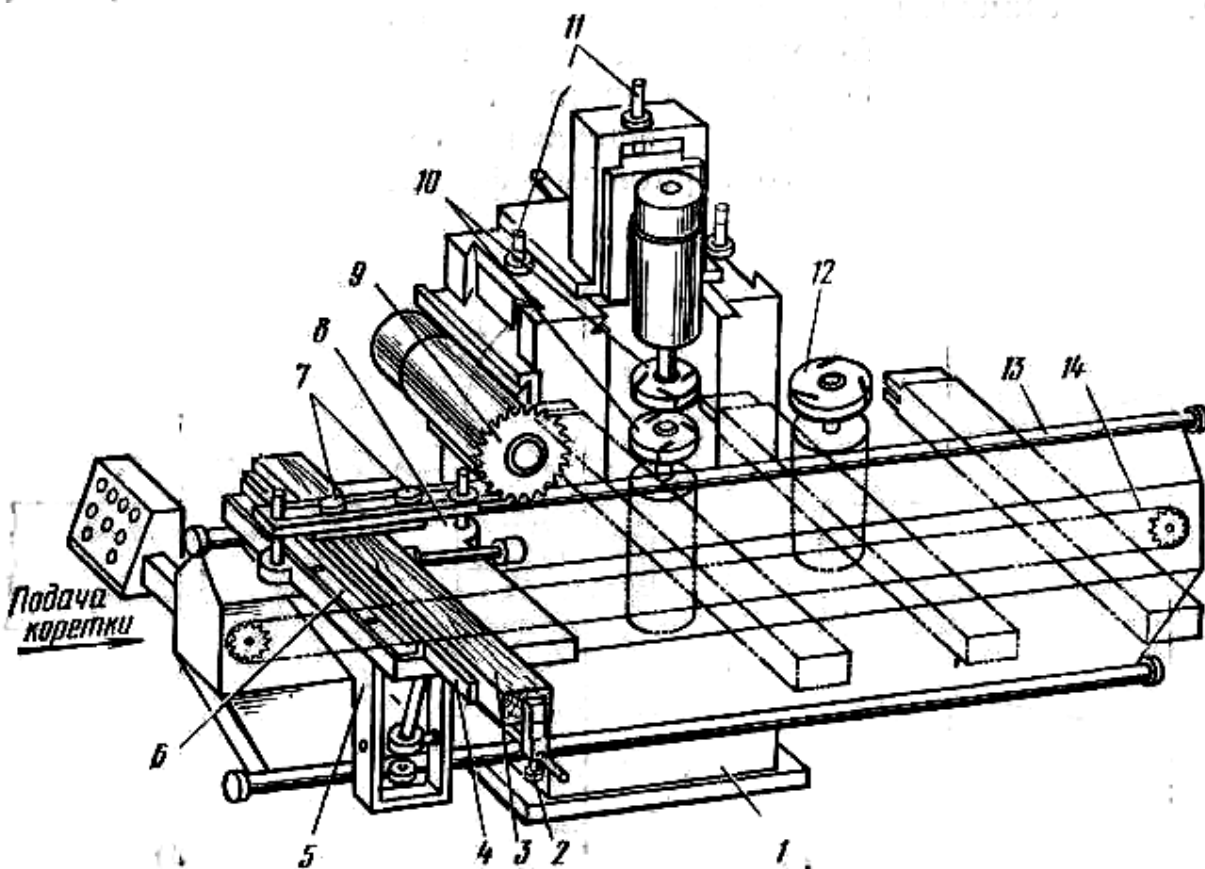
Односторонний шипорезный станок для рамных шипов ШО16-4:
